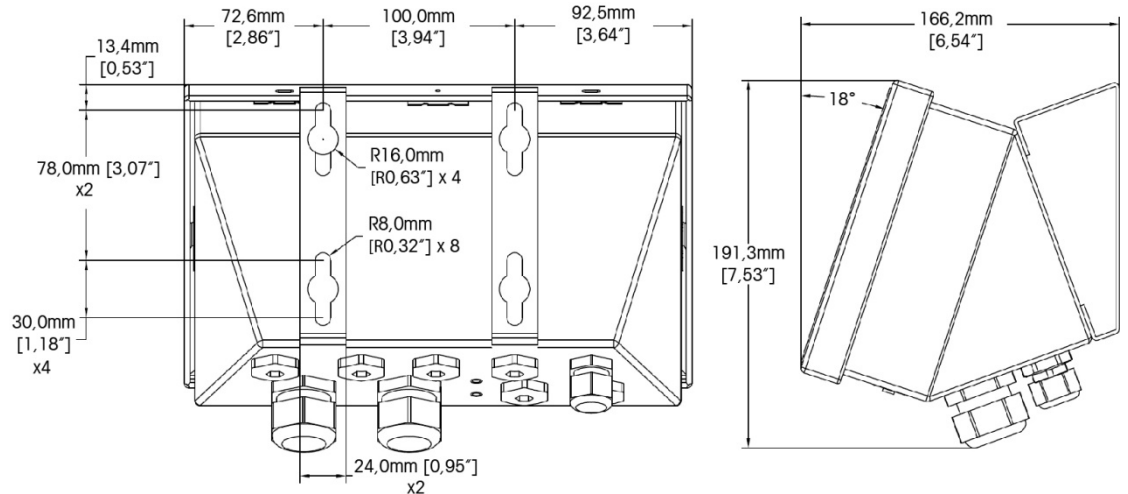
Dimensiones de la caja para ambientes adversos del IND570 con soportes de montaje de ángulo fijo, montaje original
